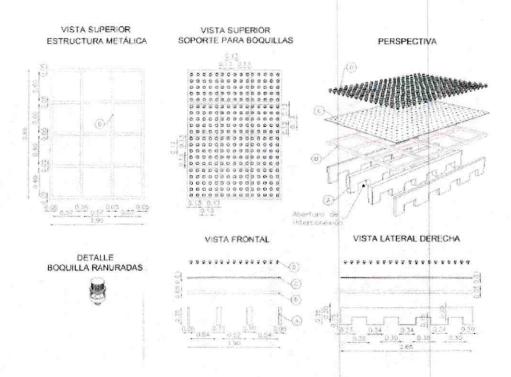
Estructura de soporte para boquillas ranuradas.
